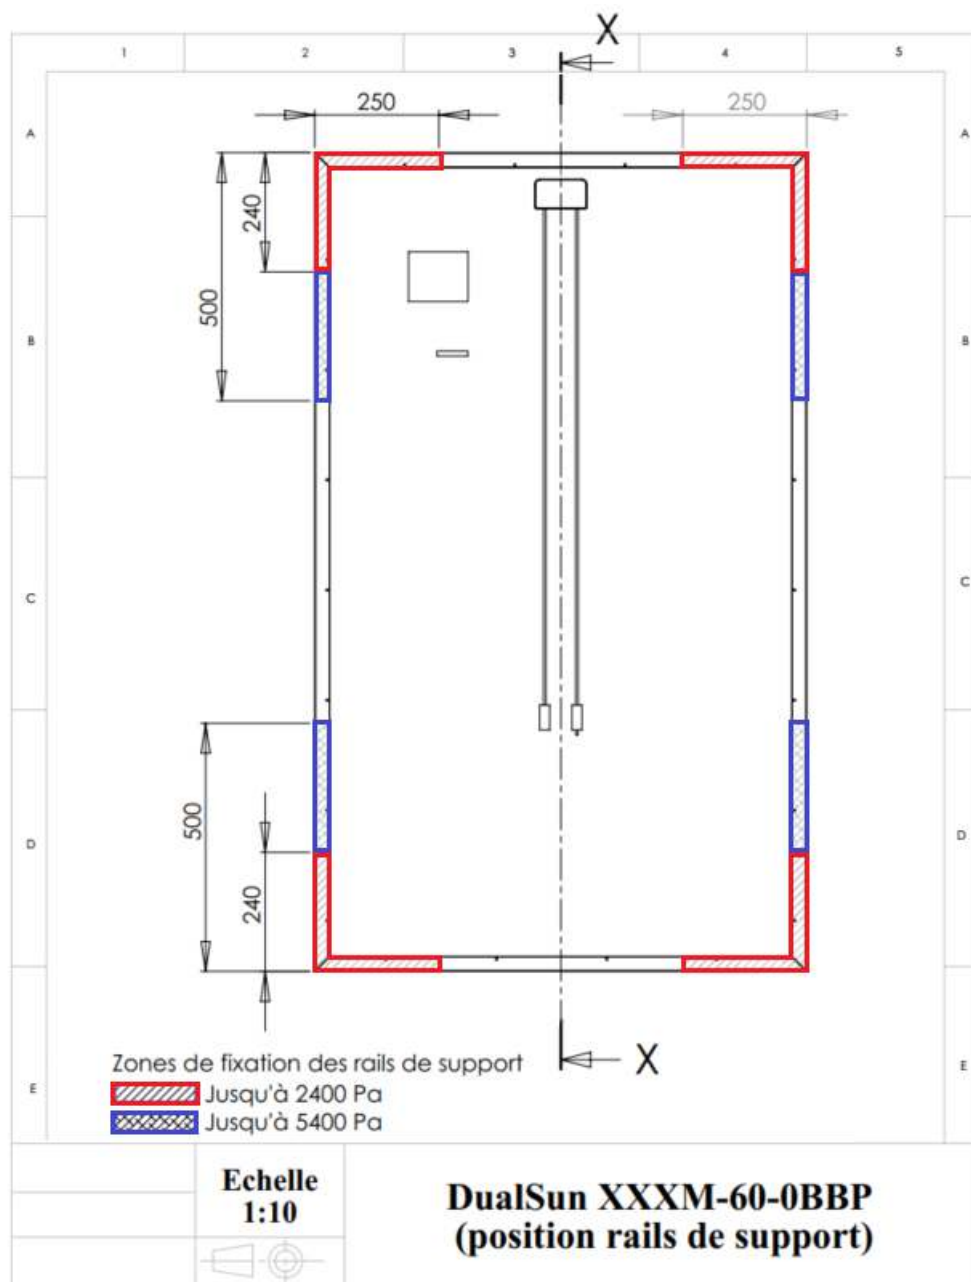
Positions possibles des étriers ou attaches de serrage du panneau Dualsun XXXM-60-0BBP
